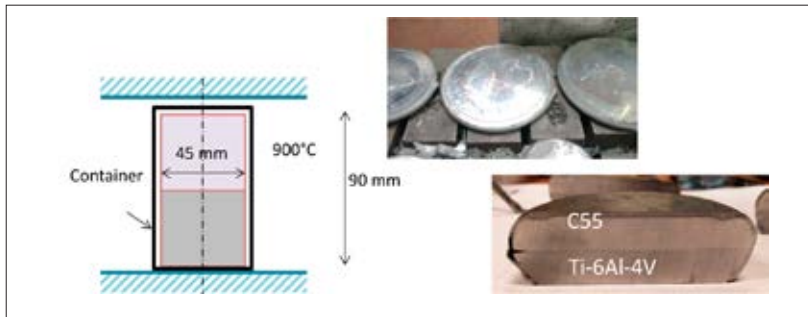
Principe de l'essai d'écrasement en container Ti-6Al-4V sur Acier
